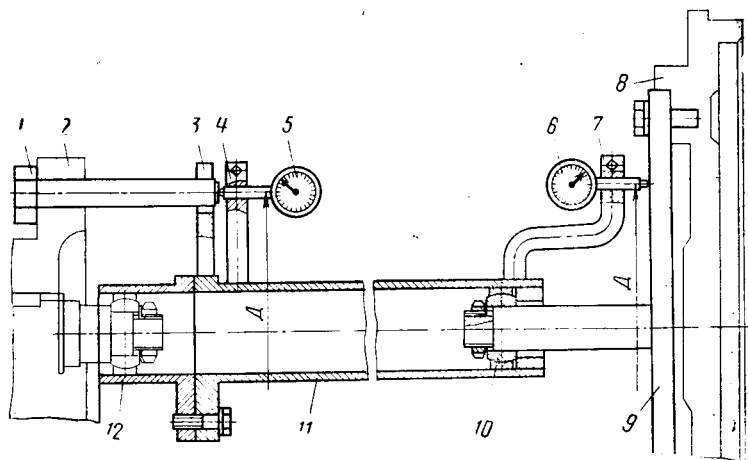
Приспособления для центровки дизеля с гидропередачей:
